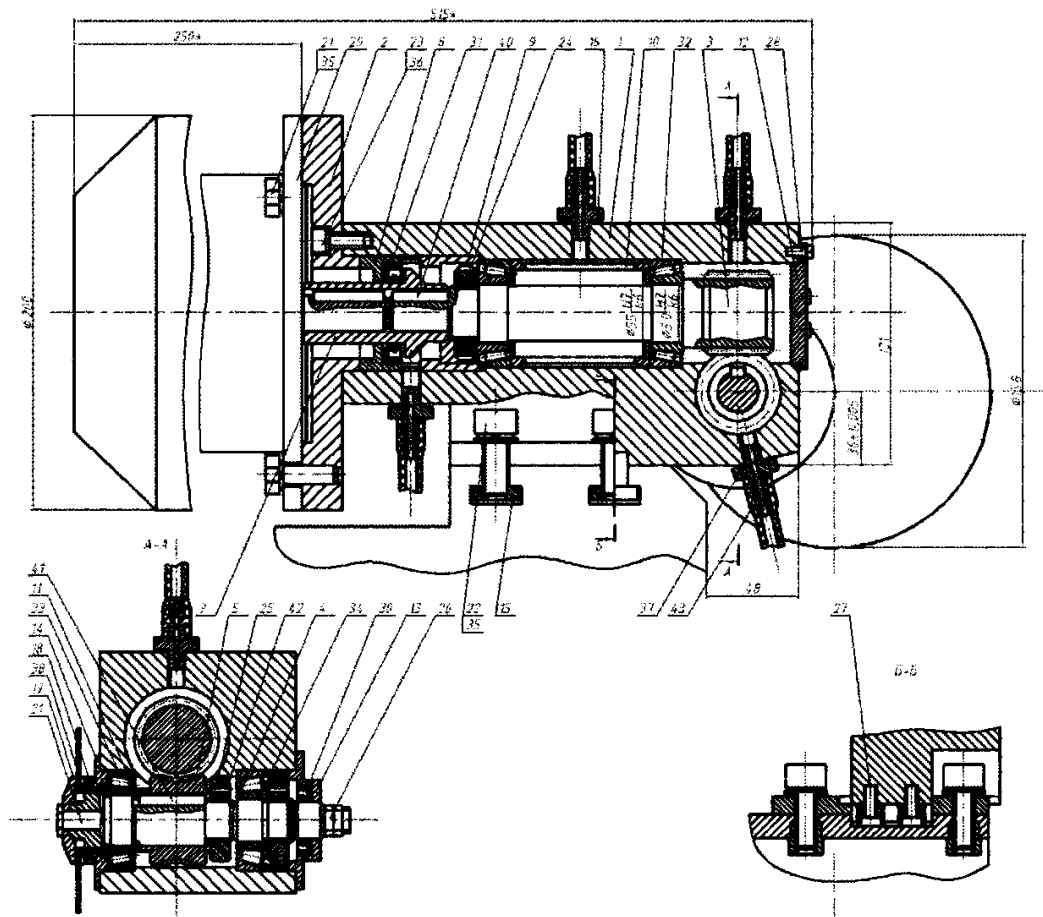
Конструкція відрізного фрезерного пристрою
